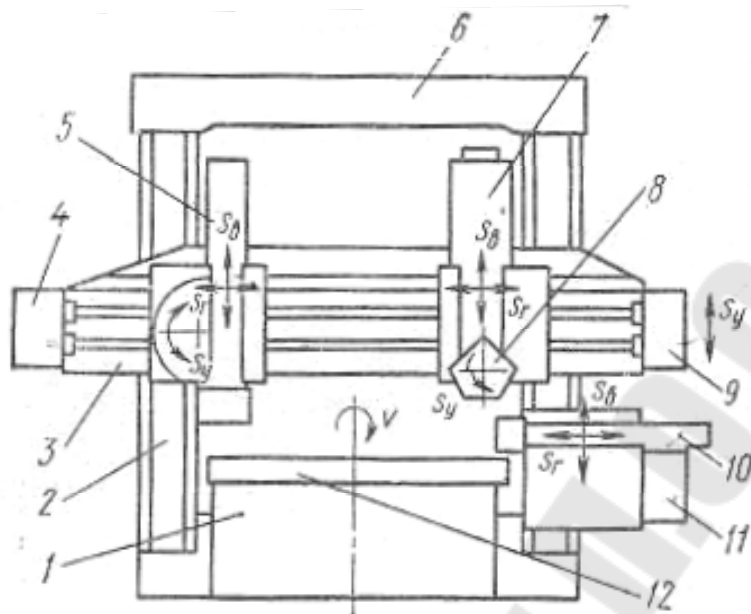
Схема двухстоечного токарно-карусельного станка:
